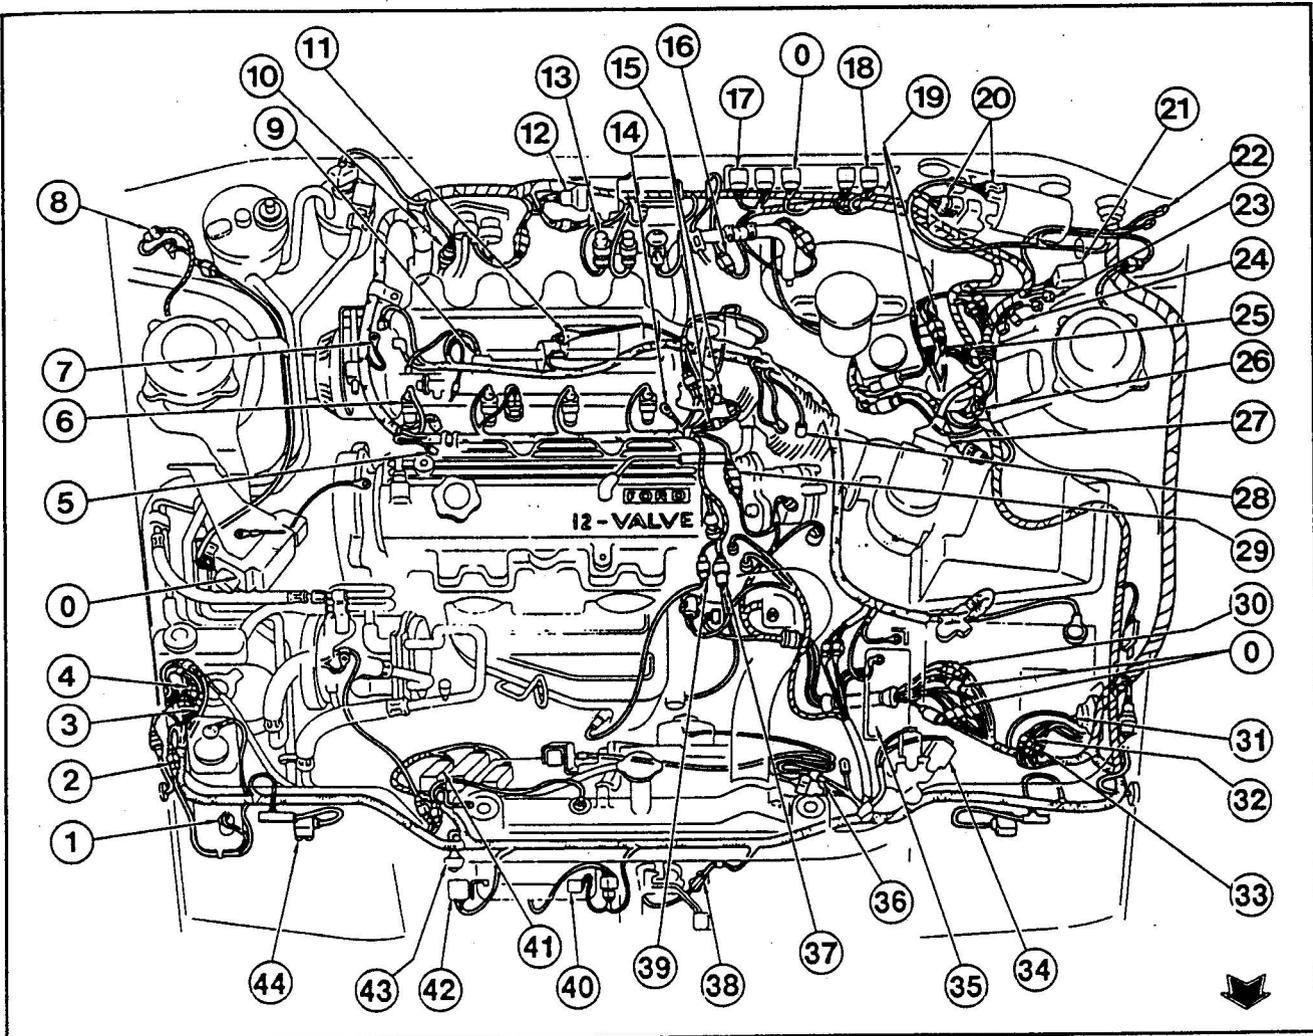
/2 Kabelstrang, Motorraum (Fortsetzung)
